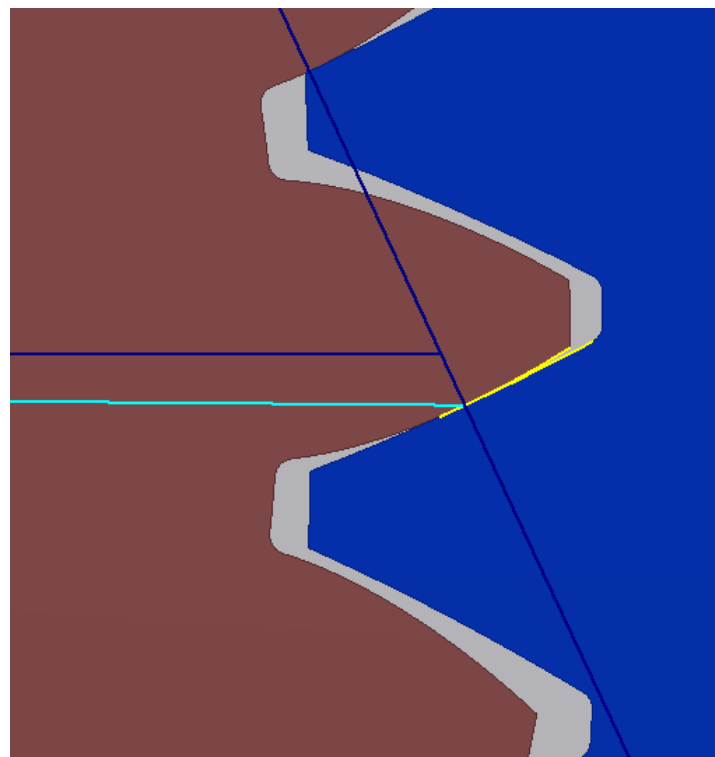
Flanco del diente en el engrane azul en contacto tangencial con la cara del diente en el engrane café.
